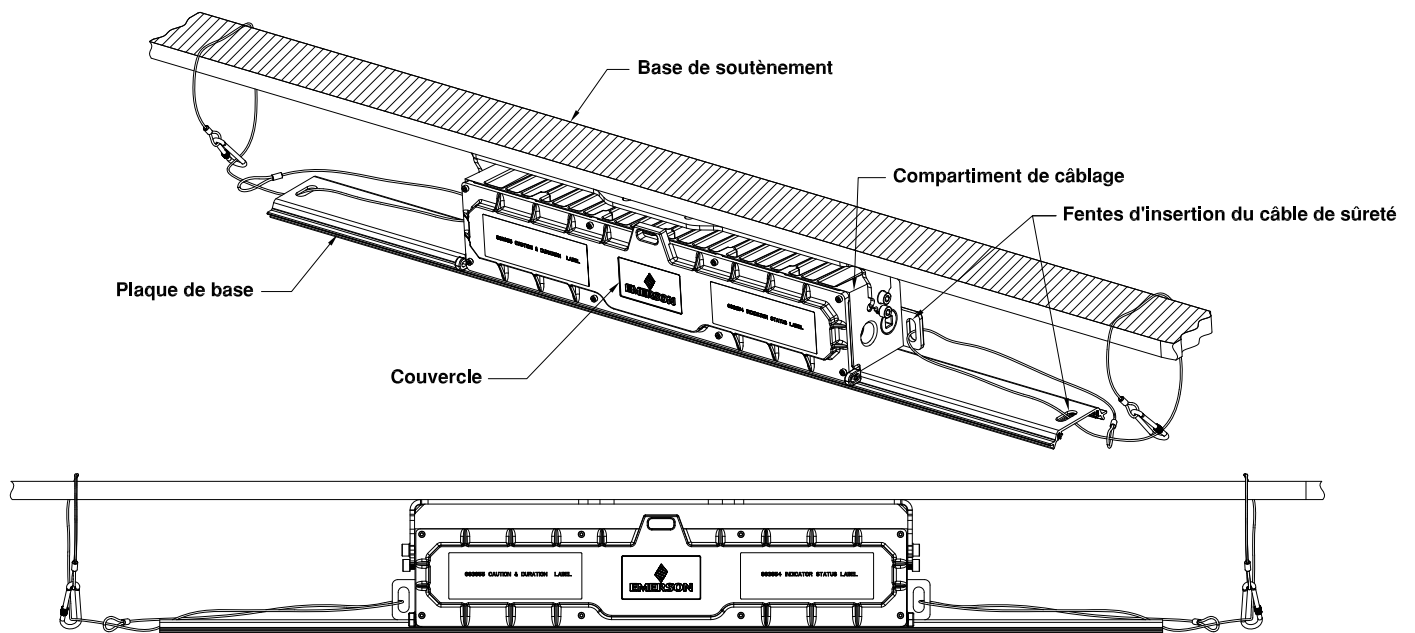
LUMINAIRE RIGMASTER 4 PIEDS AVEC CABLES DE SURETE
